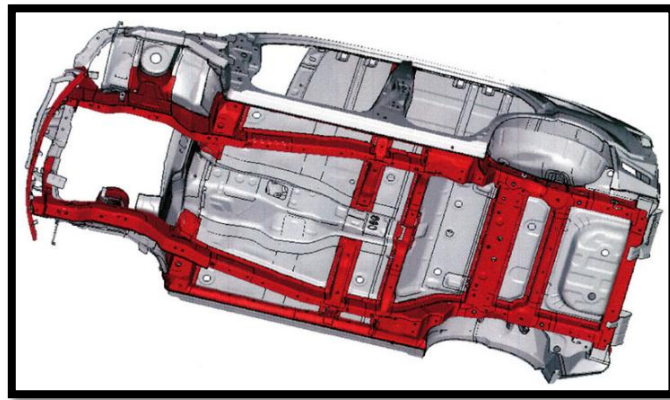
3– Carrocería y chasis separado unión soldado.
